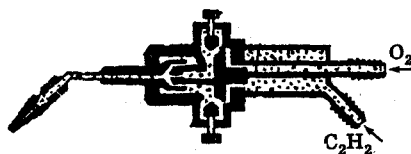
Инжекторная горелка для газовой сварки
